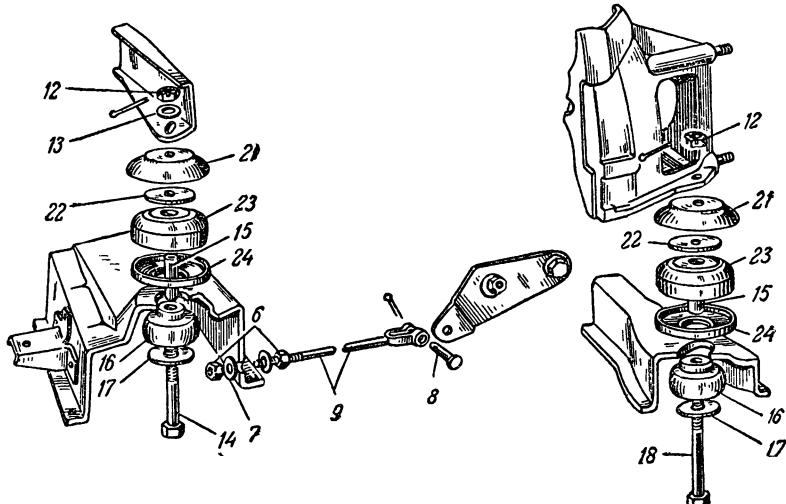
Отсоединение креплений двигателя к раме для снятия его в сборе
